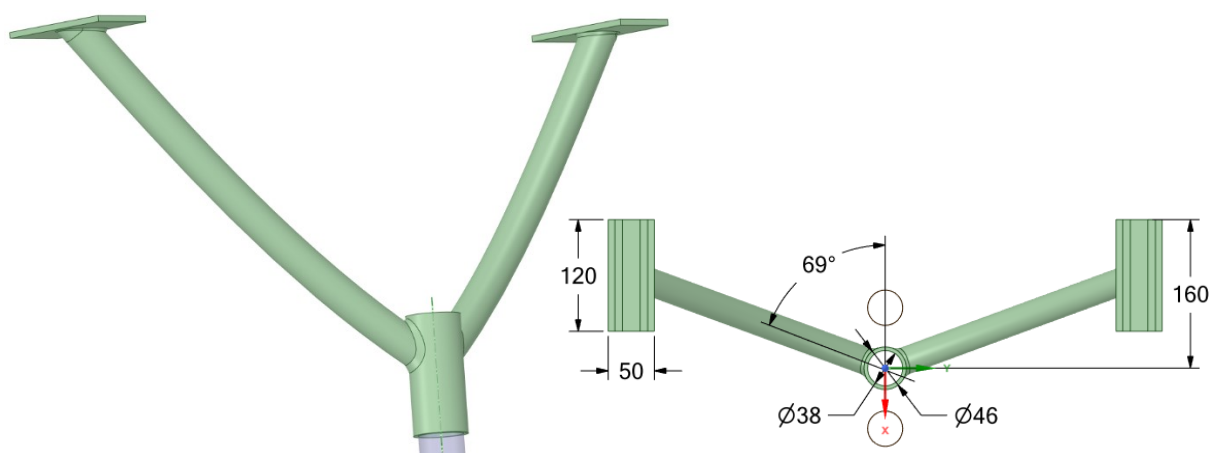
Prostředky upevnění přírub držáku k C-drážkám [9]
